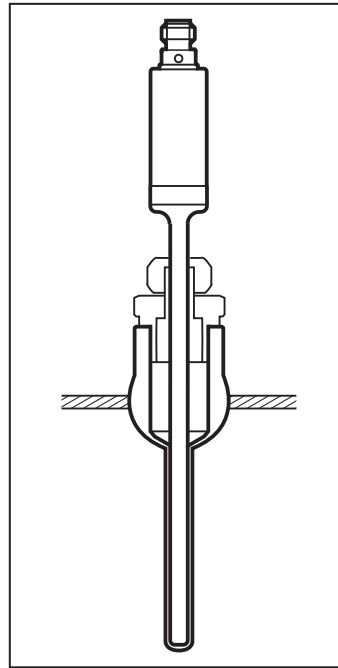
Einbau mit Schutzrohr (z.B. mit Adapter E37421)
